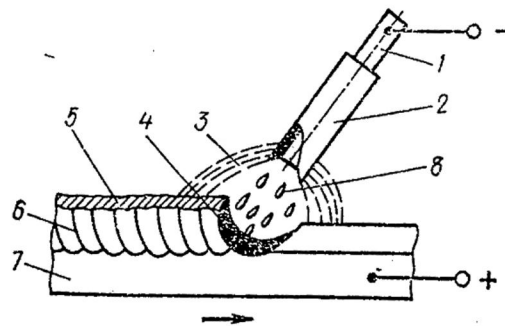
Схема ручного зварювання електродом з покриттям.
